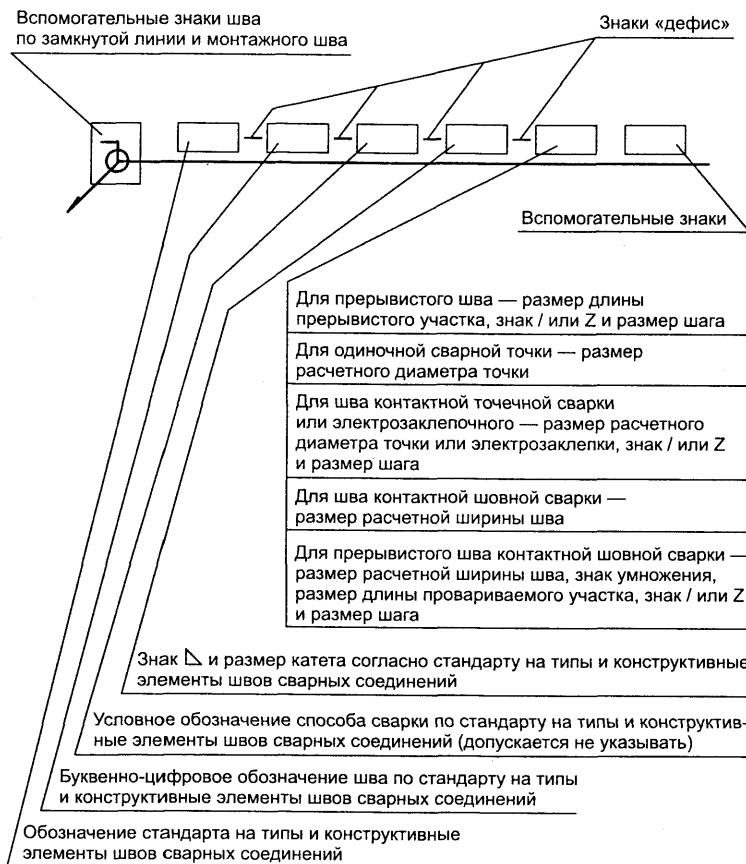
Структура условного обозначения сварного шва
